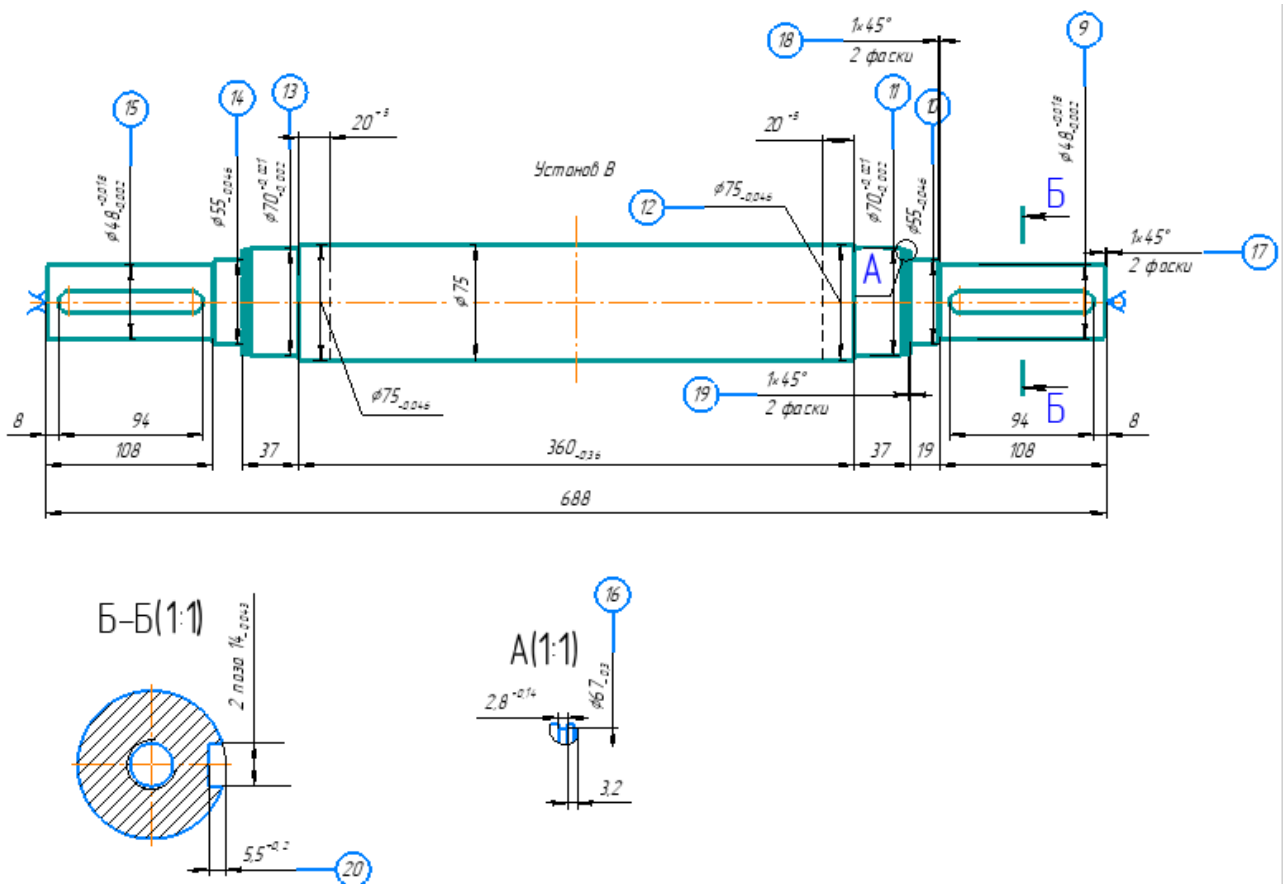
Схема базирования токарно-фрезерной с ЧПУ операции 010
